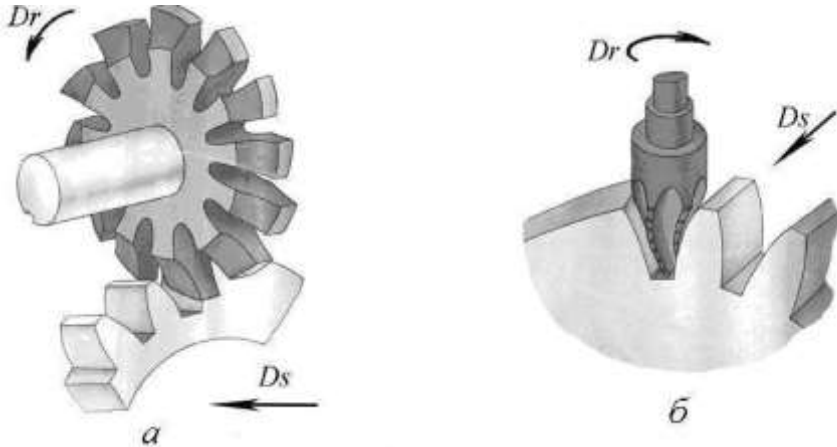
Нарізування зубців зубчастих коліс дисковою (а) та пальцевою (б) модульними фрезами
